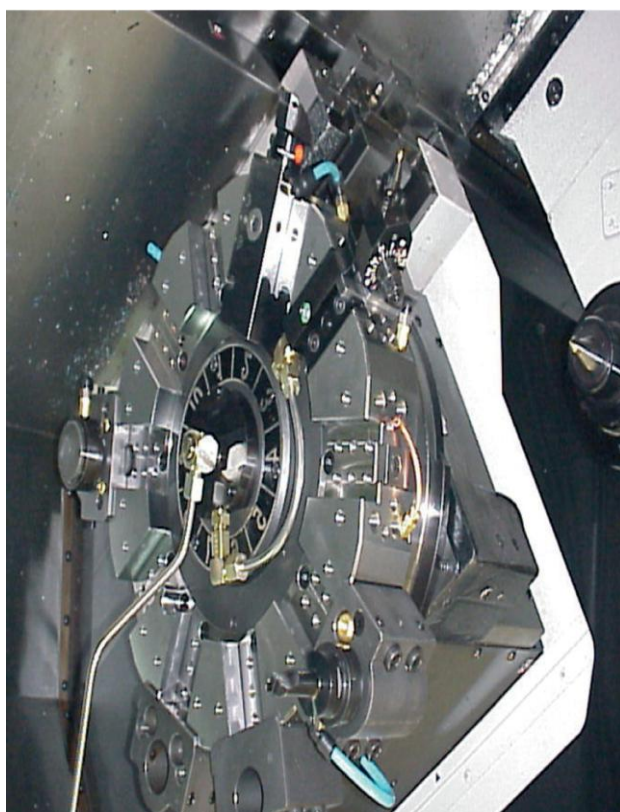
Компонировка инструмента ECOROLL в револьверной головке токарного станка с ЧПУ
